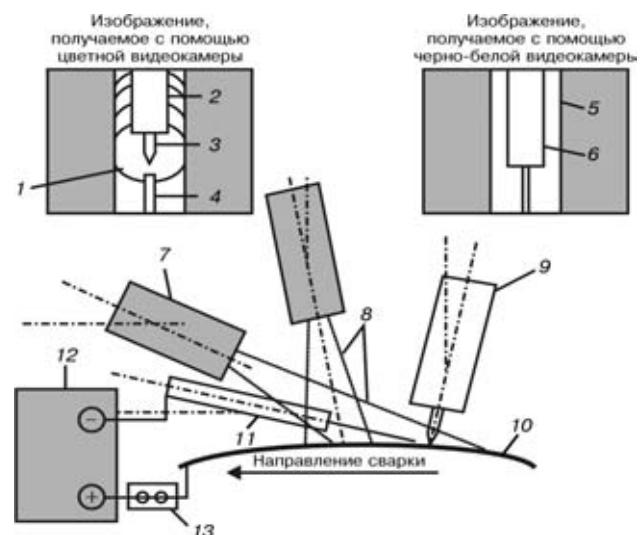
Схема расположения датчиков: 1 – сварочная ванна; 2 – горелка; 3 – электрод; 4 – проволока; 5 – притупление кромки; 6, 11 – мундштук для проволоки; 7 – цветная видеокамера; 8 – дальность контроля; 9 – сварочная горелка; 10 – труба; 12 – источник нагрева проволоки; 13 – детектор тока нагрева
